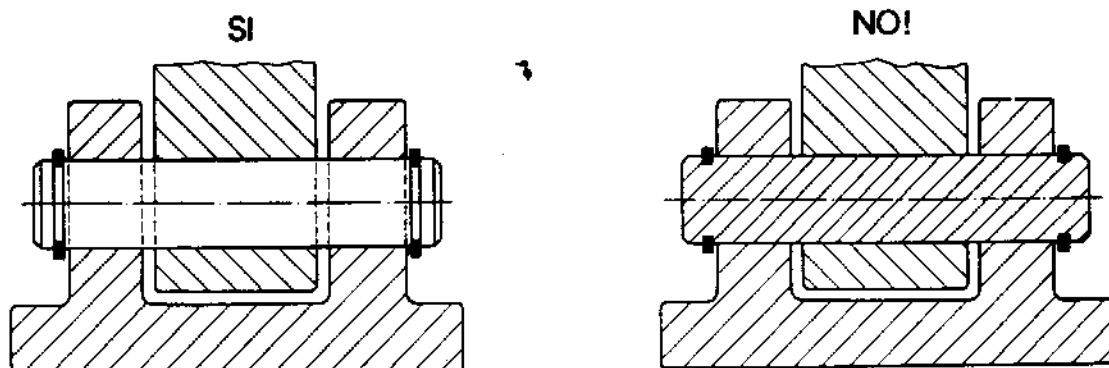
I perni non si sezionano quando il piano di sezione è longitudinale.
